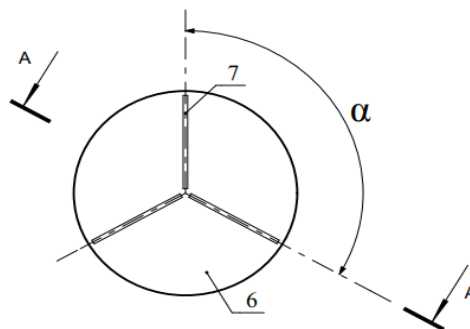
струеобразующий веерный насадок (вид с торца)
